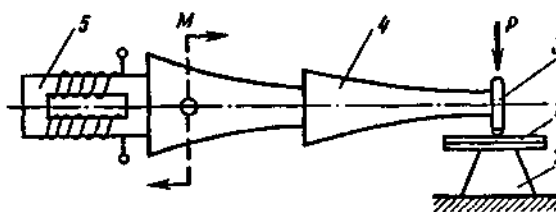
Ультразвуковая сварка: 1 – свариваемые детали; 2 – опора; 3 – наконечник; 4 – волновод; 5 – магнитострикционный преобразователь
